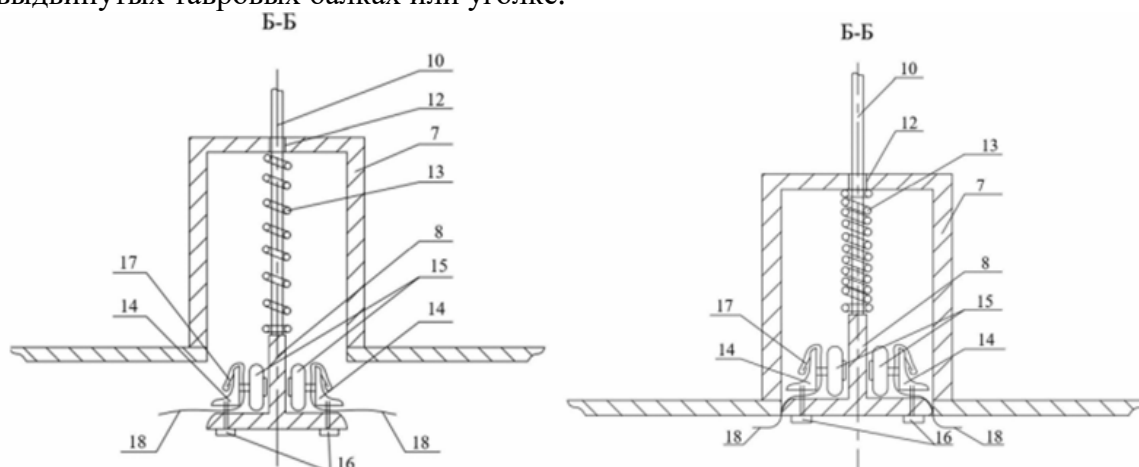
Разрез Б-Б рисунка 1, при выдвинутой и задвинутой тавровой балке: 7 – П-образный профиль; 8 – тавровая балка; 10 – шток; 12 – отверстие; 13 – пружина; 14 – рамка; 15 – колесо; 16 – фиксатор; 17 – крепежный элемент; 18 – материал с низкими адгезионными свойствами.
